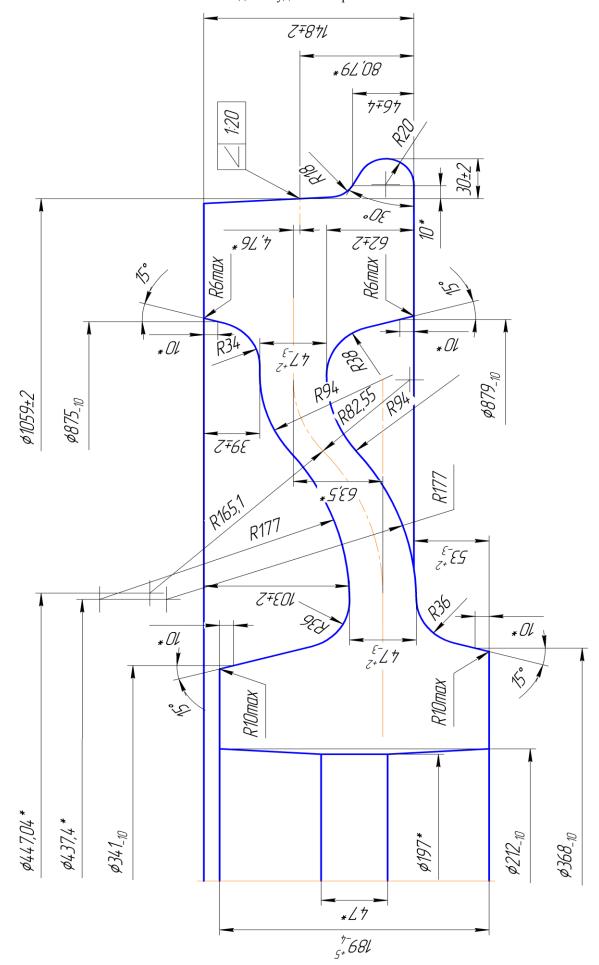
Предварительно обработанное колесо Ø1059 мм. (под чистовое Ø 1046,16 чертеж № КР-0091-12)
